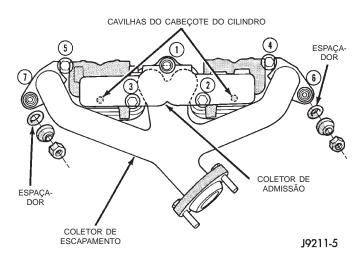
Remoção/Instalação do Coletor de Admissão/Escapamento — Motor 2.5L
